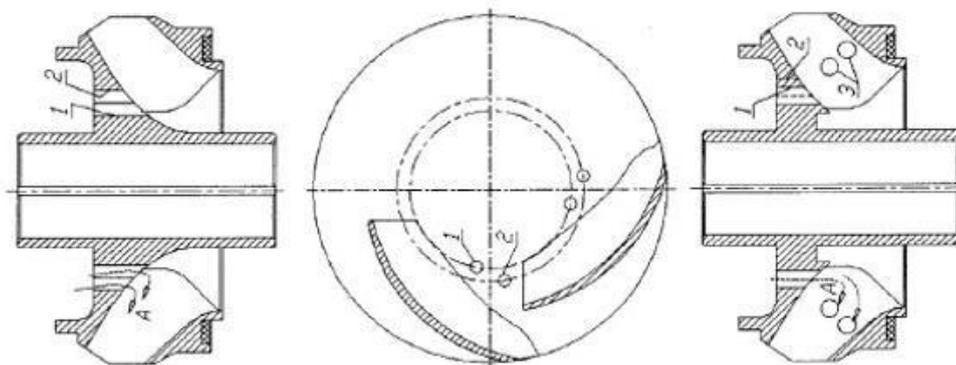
Робочі колеса диспергатора типу АГН
